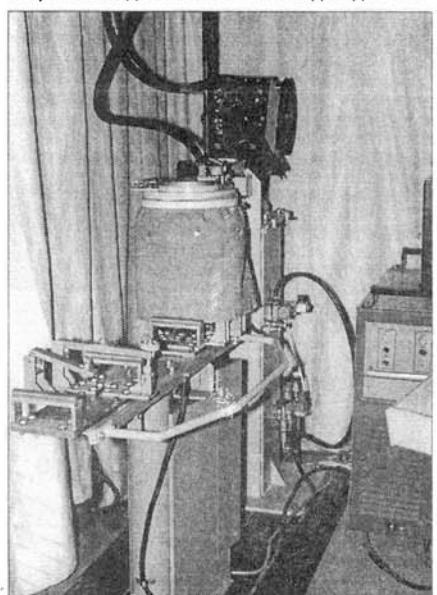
Установка для автоматической дуговой сварки бонки с подкладкой
